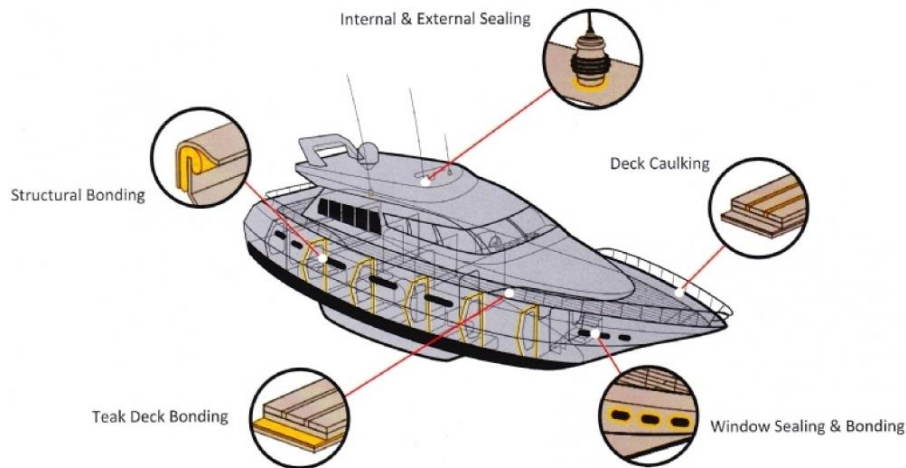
Exemplos típicos de aplicação de adesivos estruturais na construção de embarcações [14].
